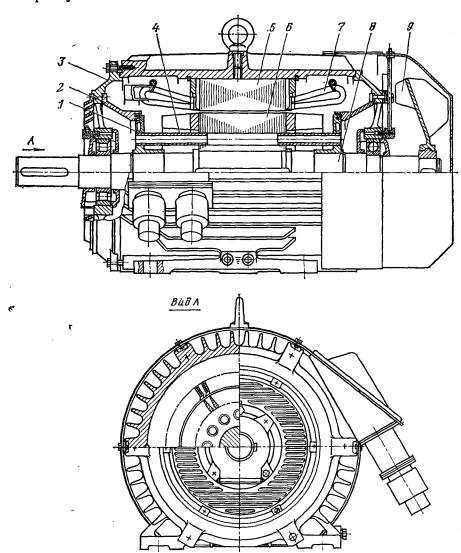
Трехфазный асинхронный двигатель исполнения ІР44 с продуваемым ротором:
